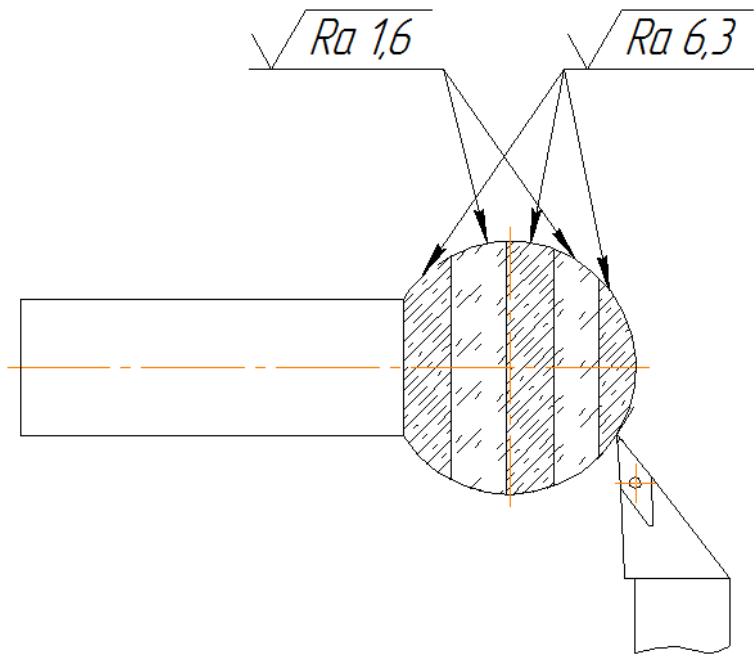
Участки и значения шероховатости сферической поверхности при обработке на токарном станке с ЧПУ
